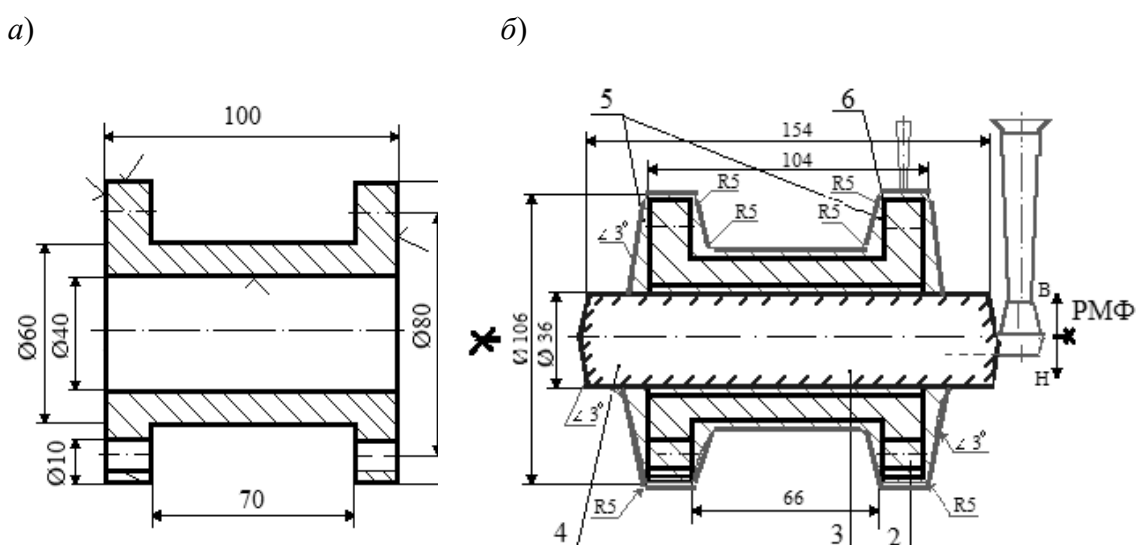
Эскизы детали (а) и технологического чертежа отливки (б)
